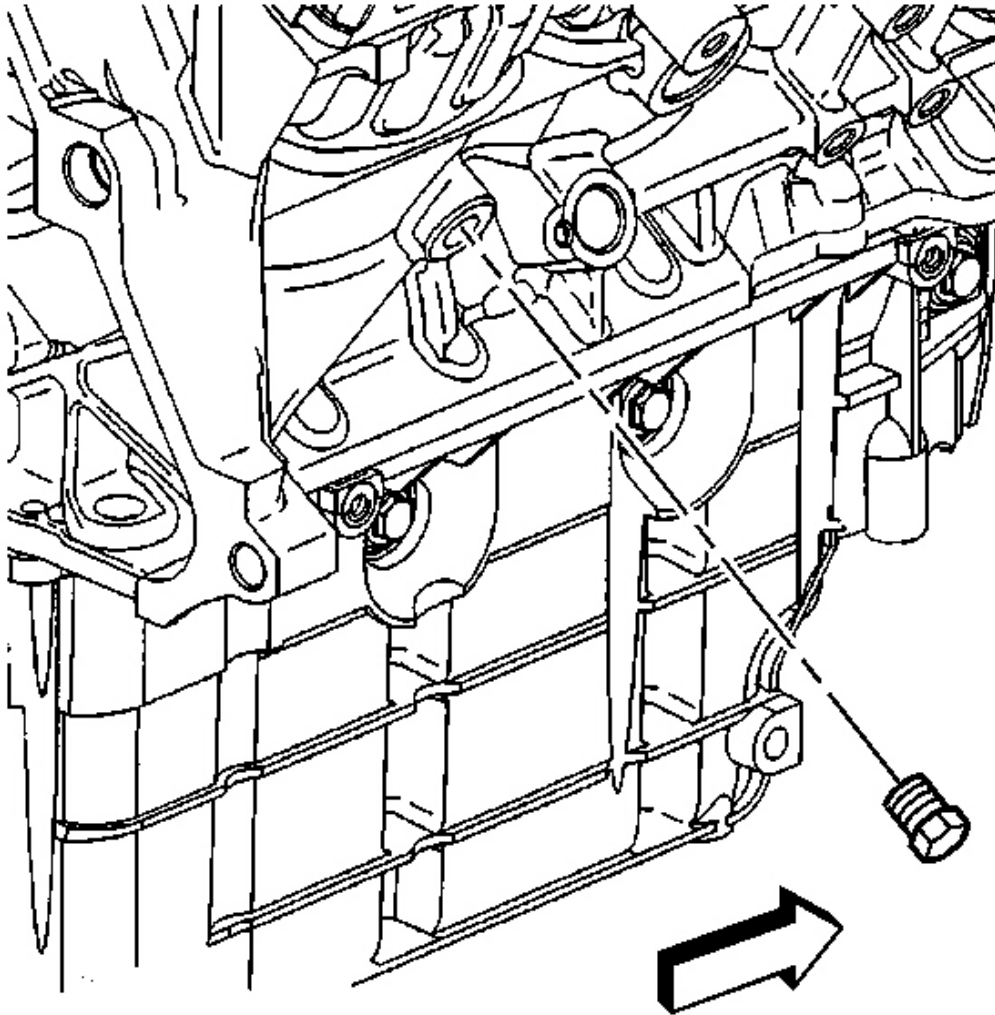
Vista de la izquierda drenaje del líquido refrigerante
